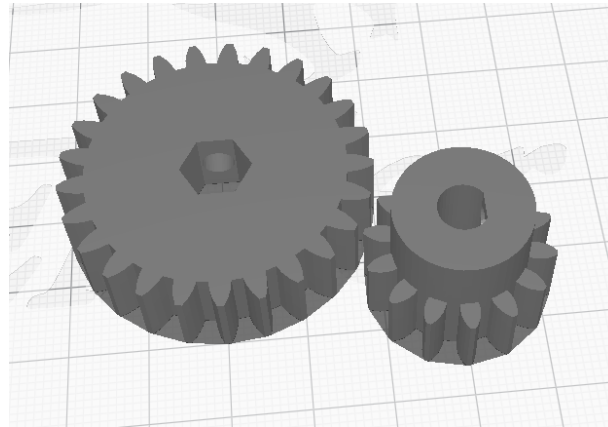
Diseño de los engranes de la transmisión reductora.
